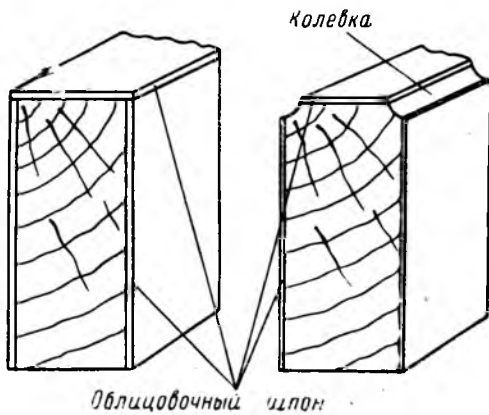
Декоративные калевки в местах стыка облицовочной фанеры
